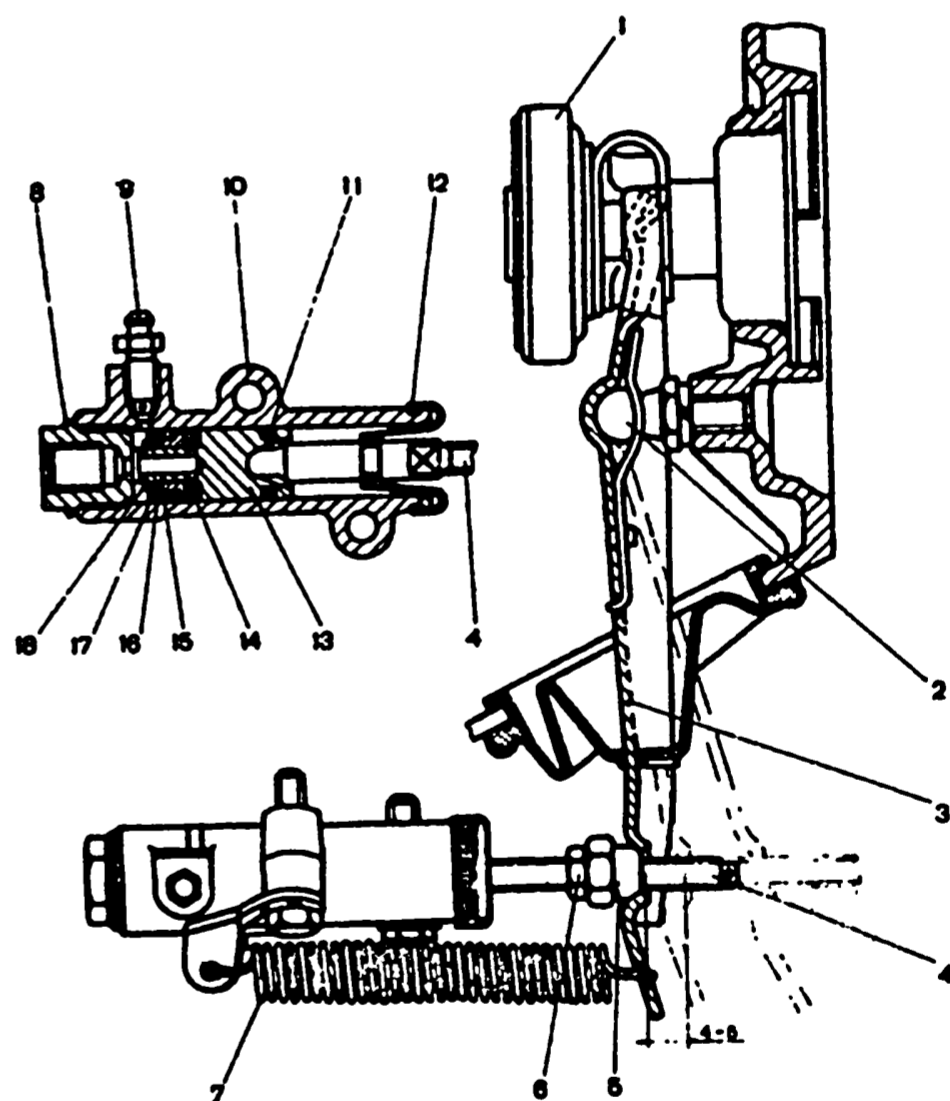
Рабочий цилиндр и вилка выключения сцепления: 1 - подшипник выключения сцепления; 2 - шаровая опора; 3 - вилка выключения сцепления; 4 - толкатель; 5 - регулировочная гайка; 6 - контргайка; 7 - оттяжная пружина; 8 - пробка корпуса; 9 - штуцер для прокачки; 10 - корпус цилиндра; 11 - уплотнительное кольцо; 12 - защитный колпачок; 13 - поршень; 14 - уплотнитель; 15 - тарелка; 16 - пружина; 17 - опорная шайба; 18 - стопорное кольцо
